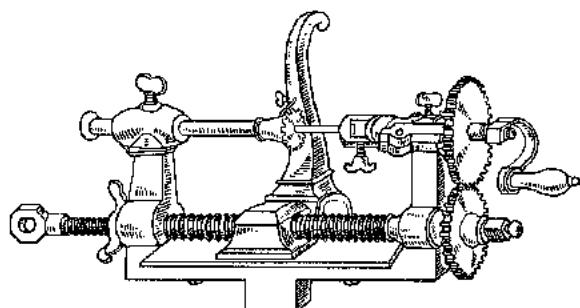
Torno francés con dispositivo de tallado de roscas, 1740 (Libro de Roe titulado "English and American Tool Builders", con permiso de McGraw-Hill Co.)
